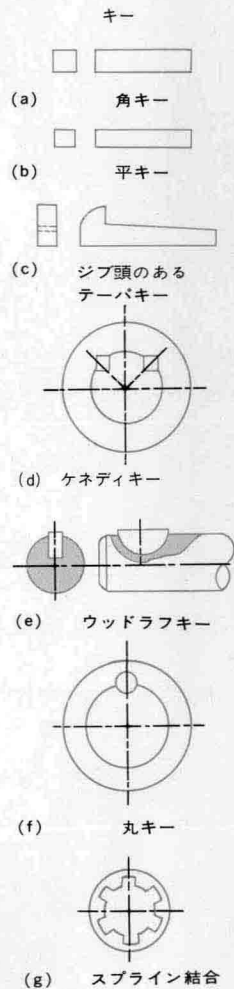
キーの型(P. H. Black and O. E. Adams, Jr., Machine Design, 1968)
